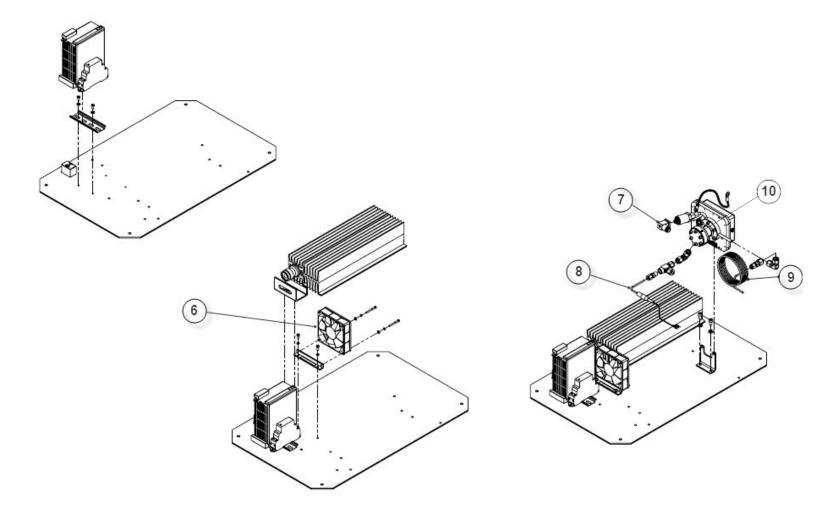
Peças para o conjunto do painel da célula da amostra 0,1 m (Continuação)
